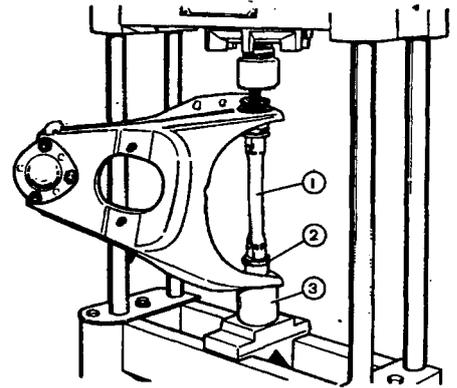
Запрессовка шарниров нижнего рычага: 1 - ось рычага; 2 - приспособление А.74177/2; 3 - приспособление А.74177/1
